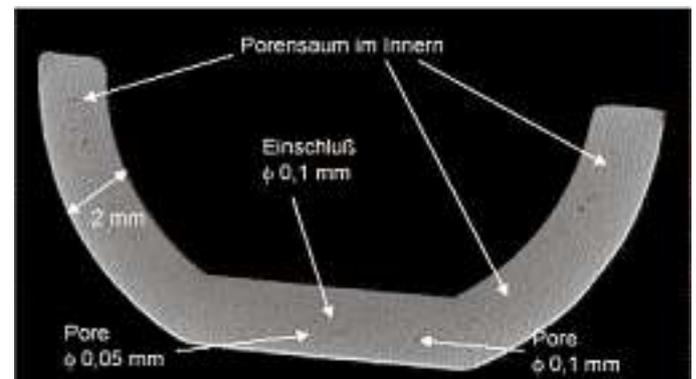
Virtueller, frontaler 2-D-Schnitt
